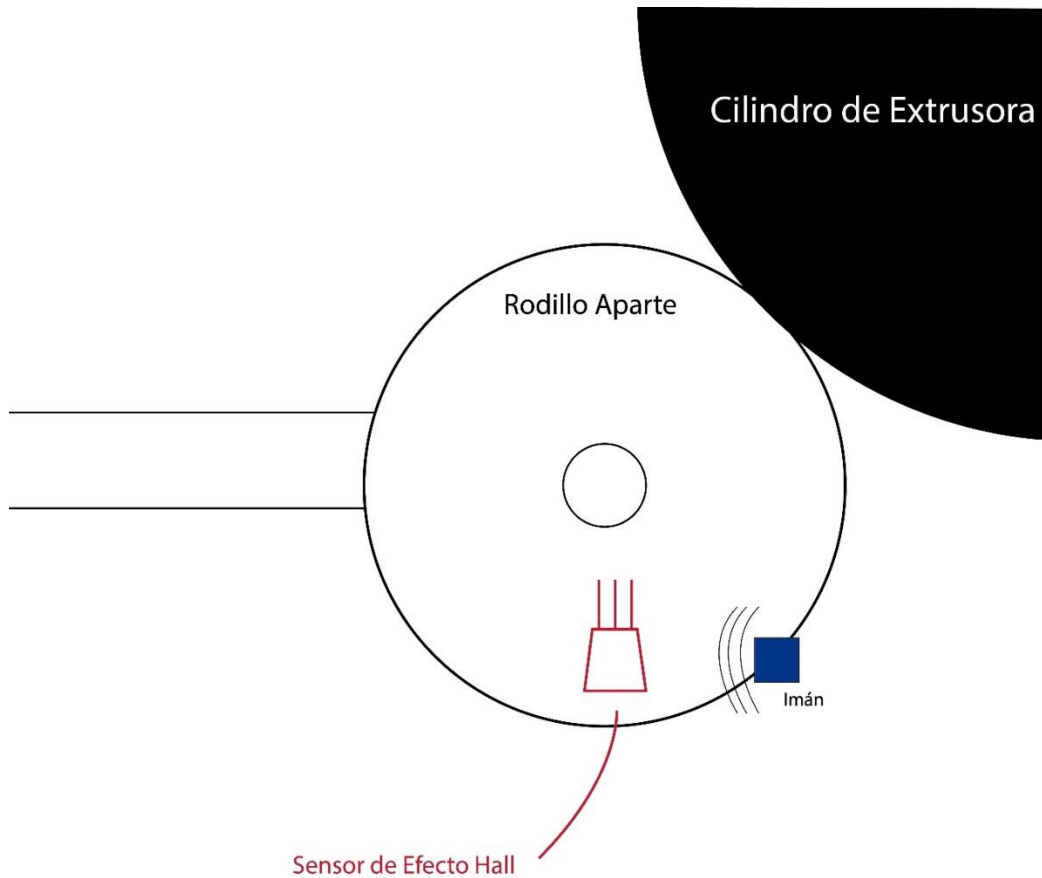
Representación visual del montaje del sensor de efecto Hall en el rodillo de la extrusora. Fuente: Elaboración propia.
